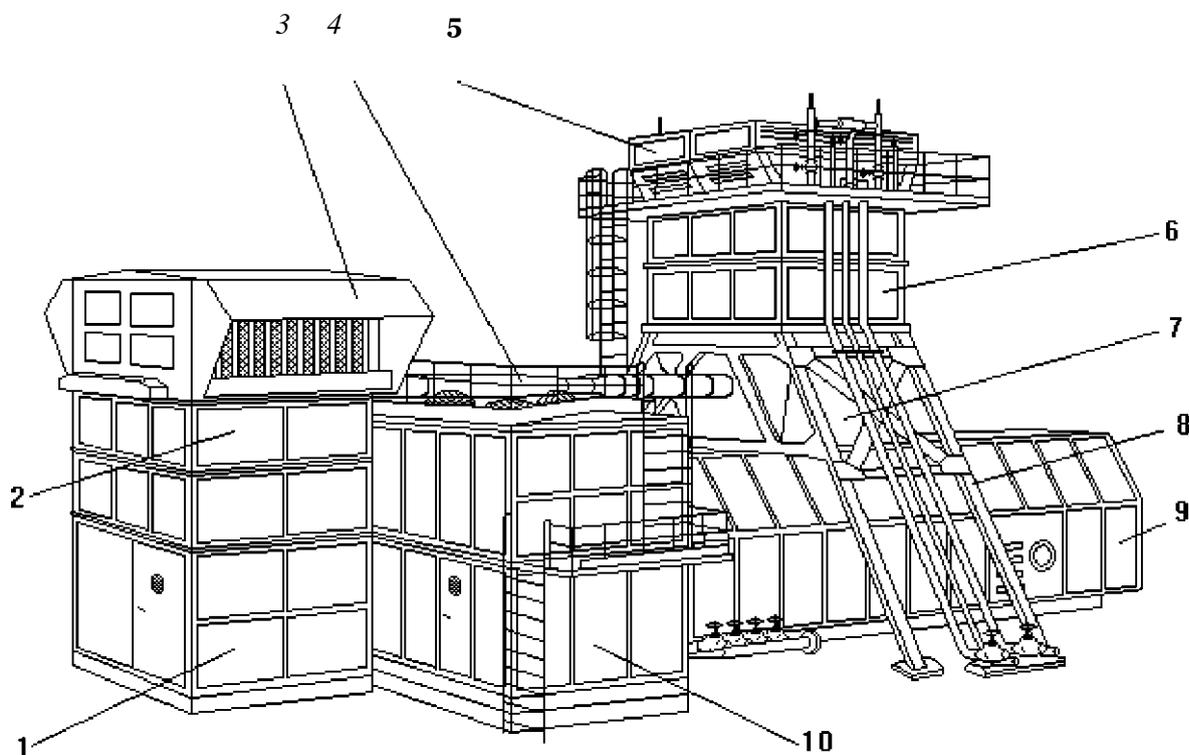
Общий вид агрегата ГПА-Ц-16: 1-камера всасывания; 2- шумоглушители всаса; 3-воздухоочистительное устройство; 4-система подогрева циклового воздуха; 5-утилизатор; 6- шумоглушители выхлопа; 7- диффузор; 8-опора выхлопной части; 9-турбоблок; 10-блок маслоагрегатов
